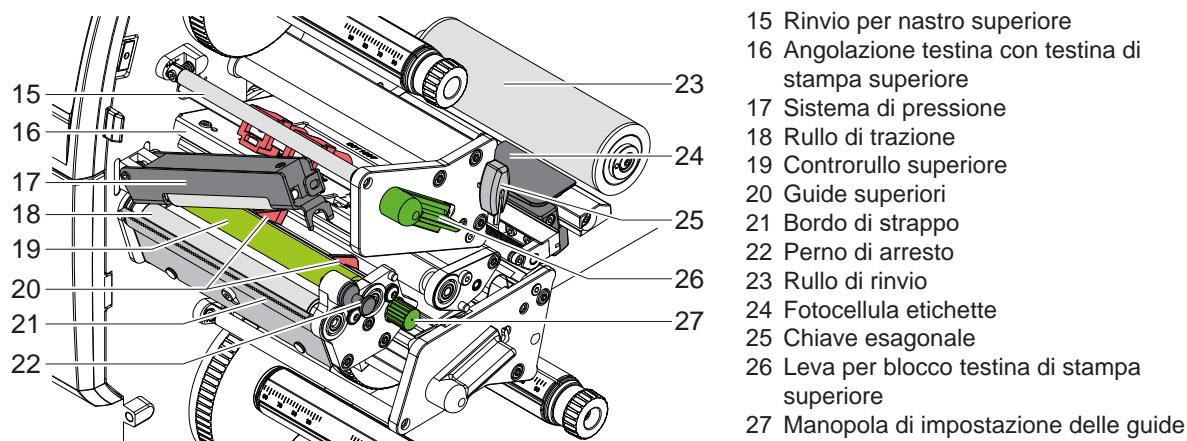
Meccanica di stampa - Gruppo di stampa superiore
